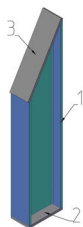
Деталь 4. Ограничитель продольного смещения стеновой панели:
